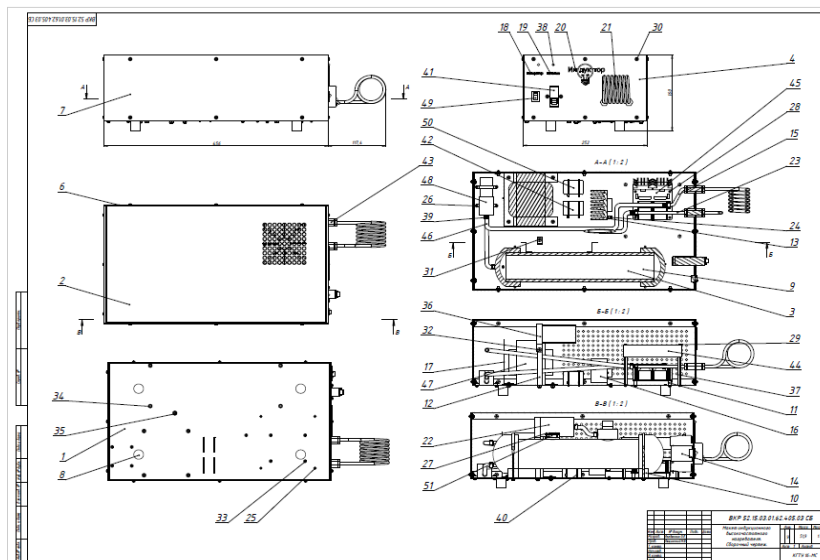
Сборочный чертеж макета индукционного высокочастотного нагревателя
